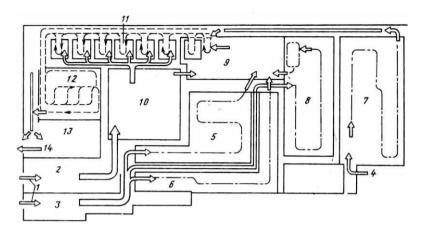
Схема компоновки корпуса по производству деталей двигателей со стендовой сборкой и указанием схемы транспортных связей
